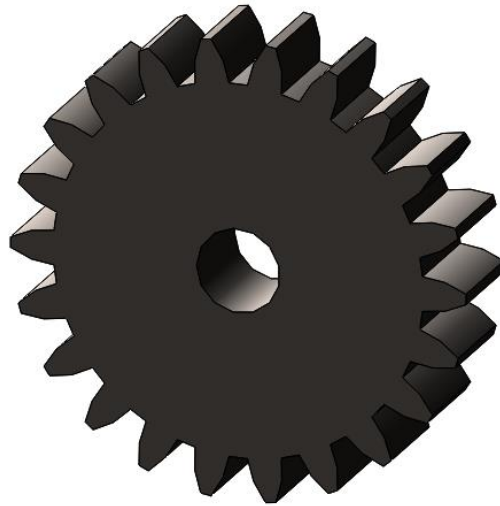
Modelo virtual tridimensional del engranaje diseñado con Toolbox
